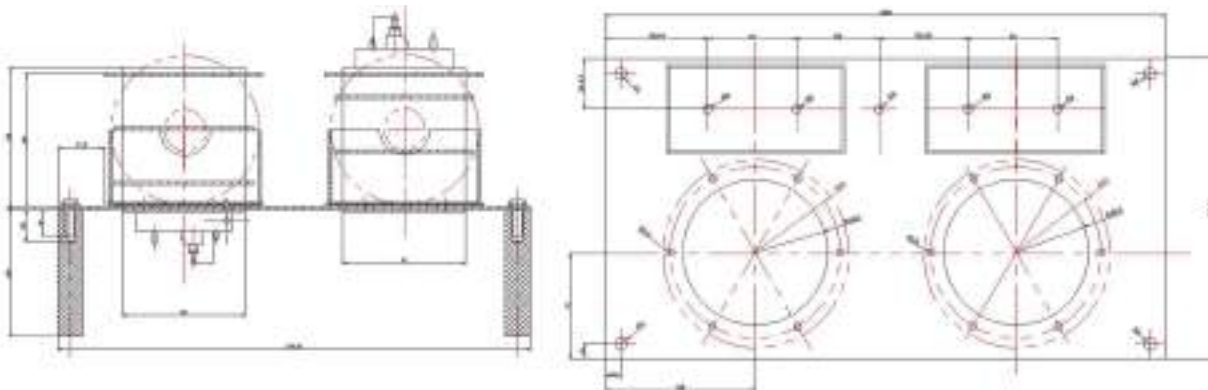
Пример сборочного чертежа конструкции генератора инфлекторов, выполненный в AutoCAD.
